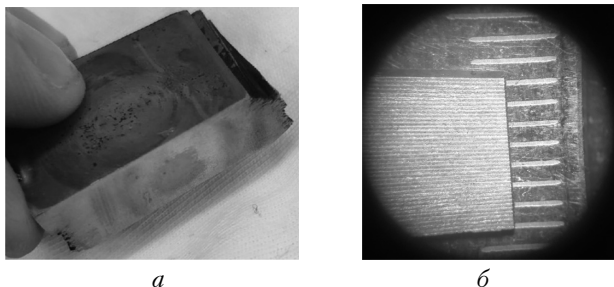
Заготовка после диффузионной сварки (*a*) и готовый ГГДТП (*б*)
